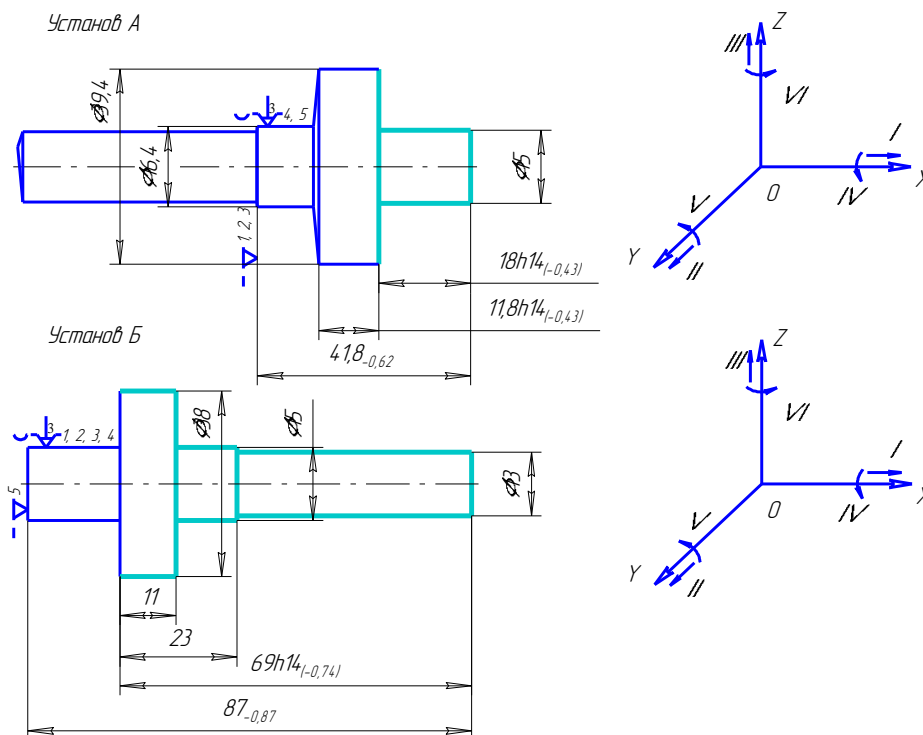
Базування заготовки на операції 015 за схемою №2
